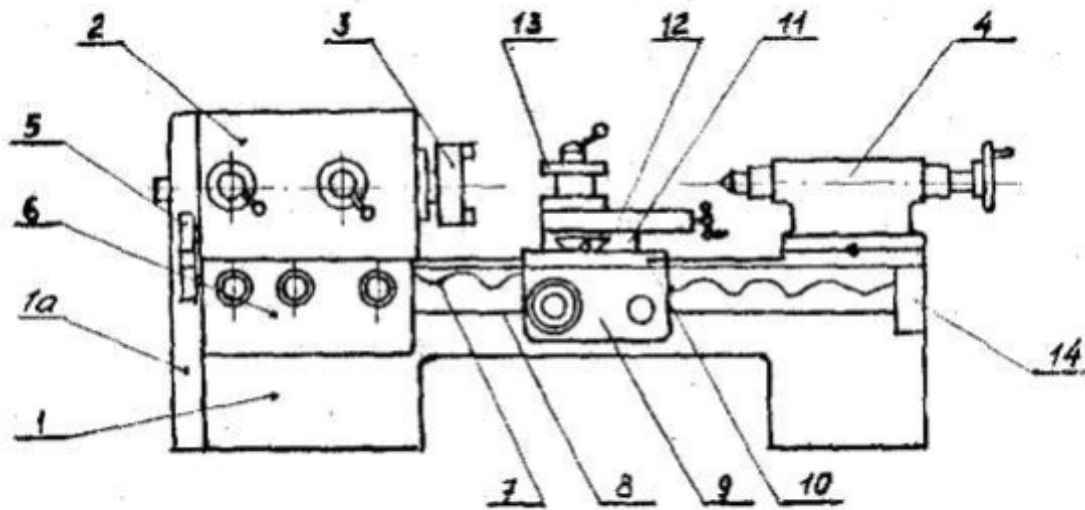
І. Універсальний токарно-гвинторізальний верстат
